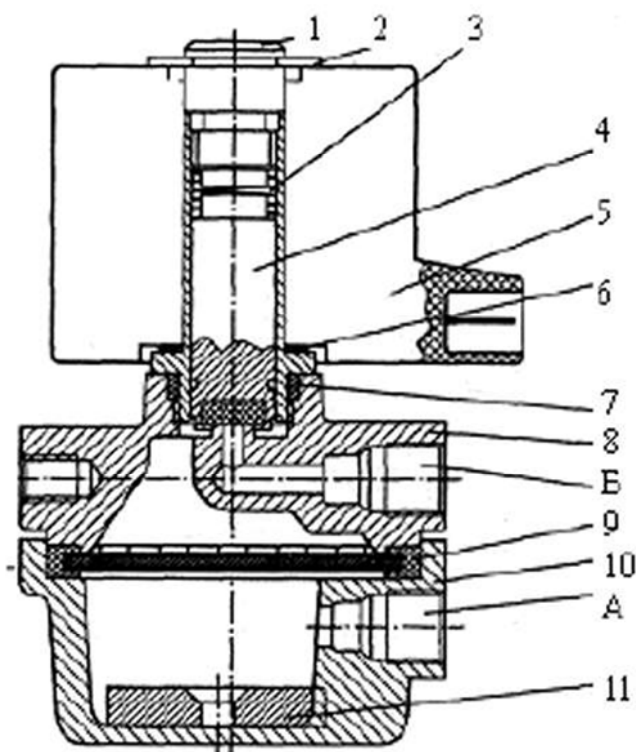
Электромагнитный газовый клапан: 1 - втулка направляющая; 2 - стопорная шайба; 3 - пружина; 4 - якорь; 5 - катушка; 6 - кольцо пружинное; 7 - кольцо уплотнительное; 8 - корпус; 9 - фильтр; 10 - отстойник; 11 - магнит; А - вход газа; Б - выход газа
